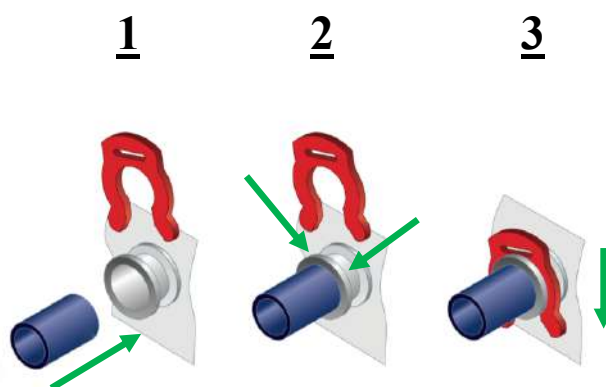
Подключение трубок к быстросъемным фитингам на корпусе Установки.
